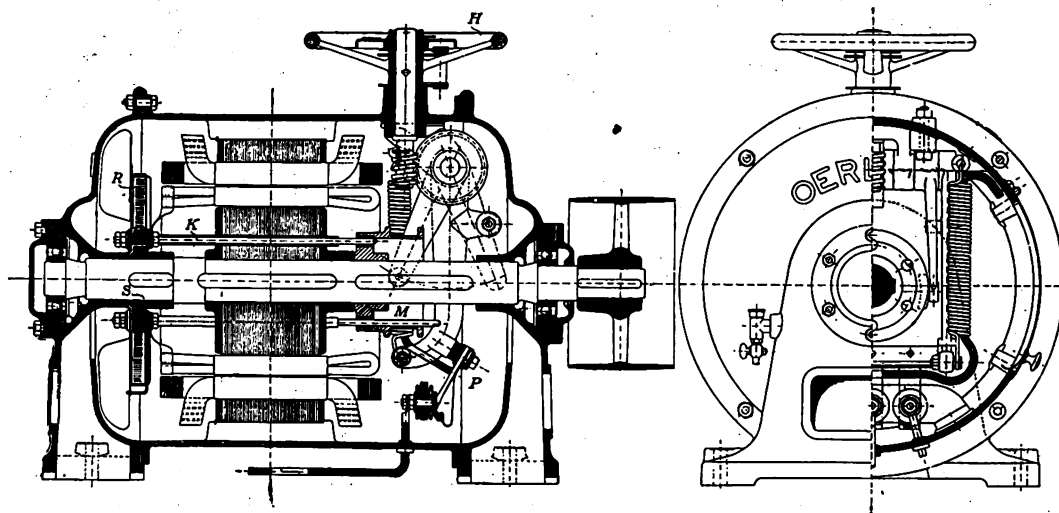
Sections longitudinale et transversale d'un moteur triphasé, type blindé.
